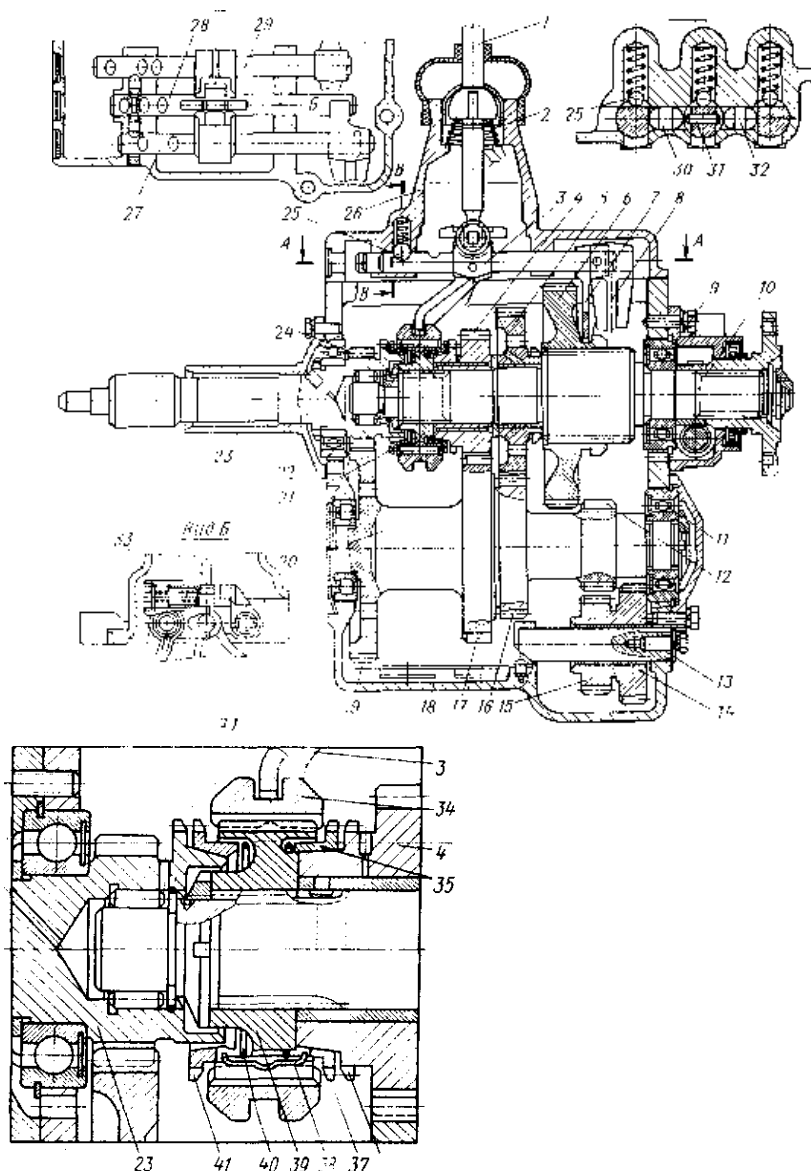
Коробки передач автомобиля ГАЗ-53А: а – общий вид; б – синхронизатор; в - положение зубьев синхронизатора при блокировке
